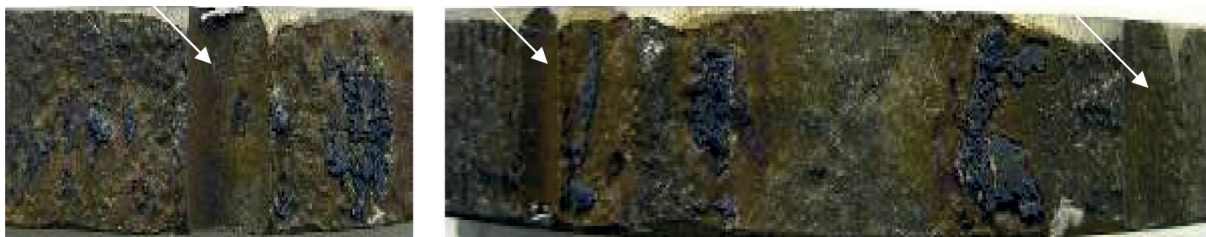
Внешний вид рисок на поверхности непрерывнолитых заготовок диаметром 200 мм
